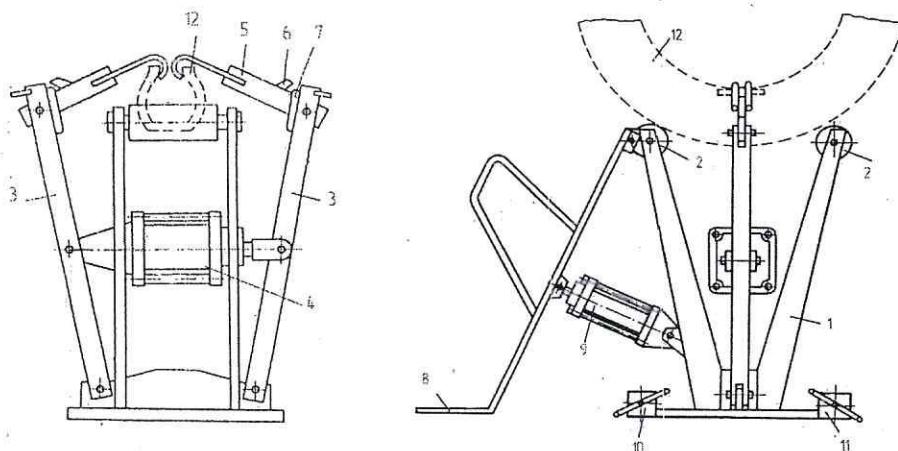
Устройство для осмотра и ремонта покрышек
